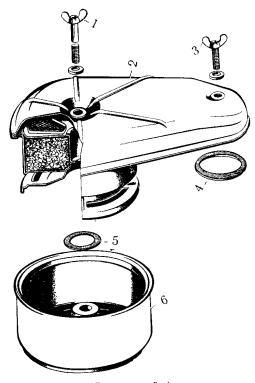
Воздушный фильтр: 1 и 3 — вииты-барашки; 2 — крышка с фильтрующим элементом; 4 и 5 — прокладки; 6 — корпус фильтра
